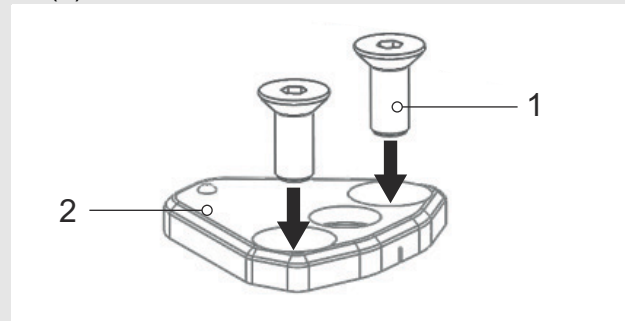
Senkkopfschrauben in Basisplatte stecken
